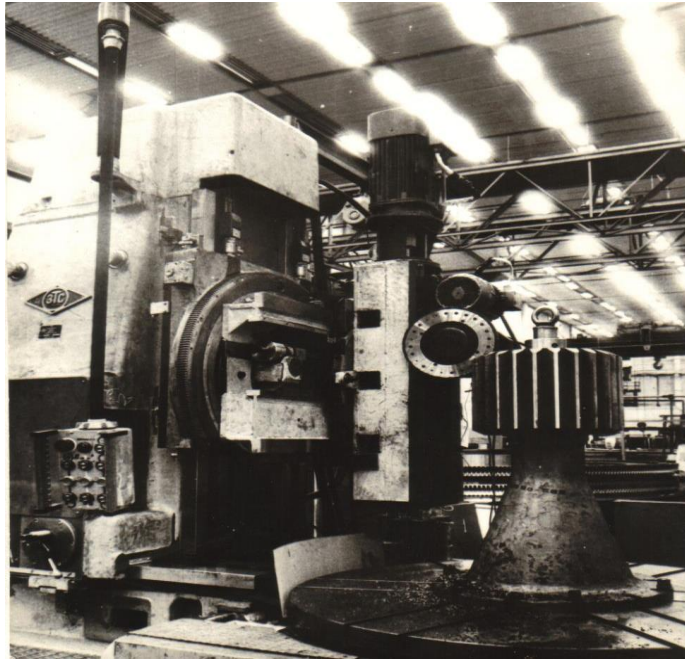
Обробка зубів, що загартовані, з застосуванням одношпindelного спецсупорта та дискових фрез на зубофрезерном верстаті мод. 5А342
